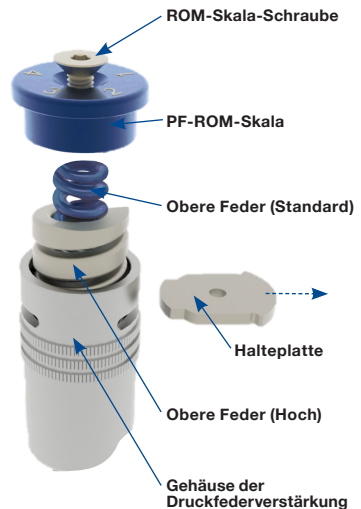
Entfernen Sie die Halteplatte und richten Sie die gewünschte Federkonfiguration ein.
